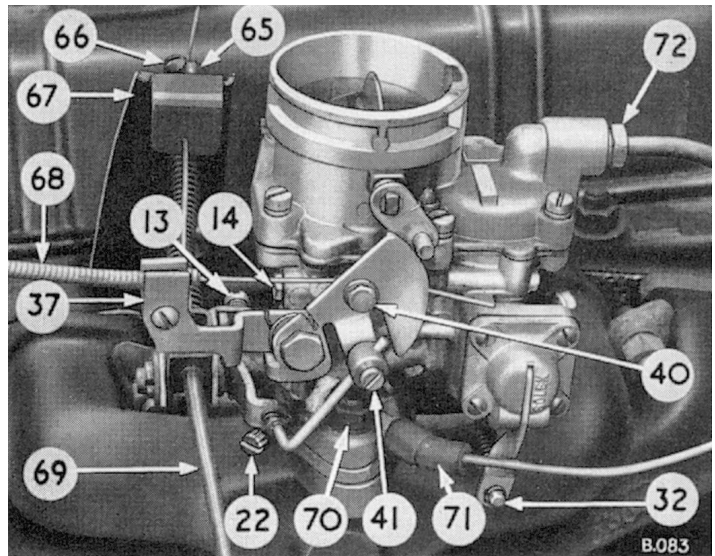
Carburateur B30 PSE1 : vue détaillée
